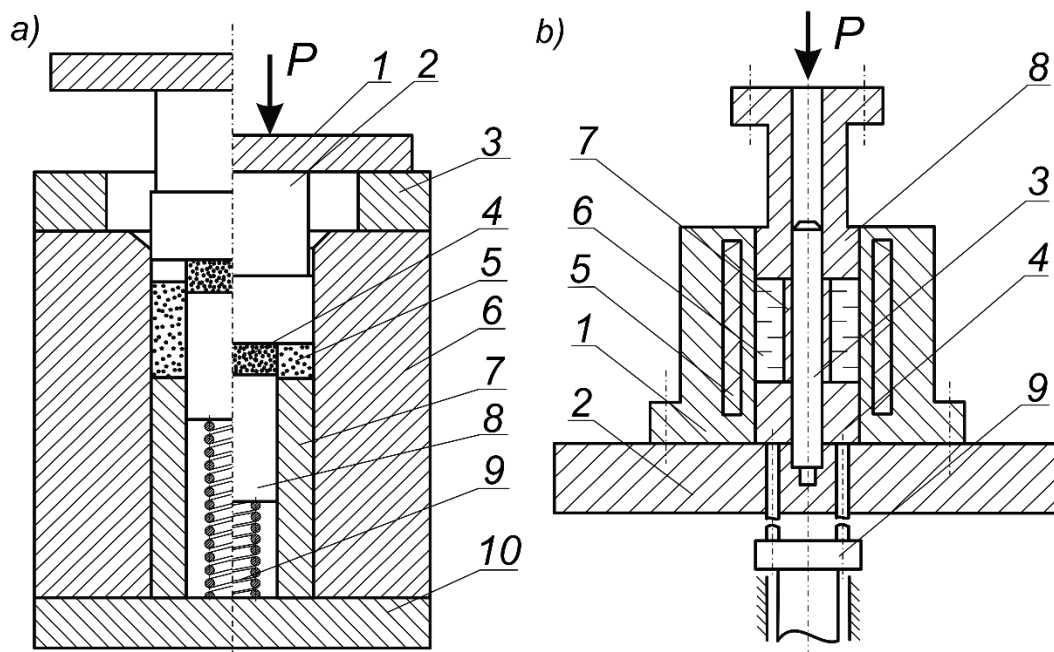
Принципиальные схемы пресс-форм. Схема для прессования спеченных вкладышей с порошком (а): 1 - плита, 2 - верхний пуансон, 3 - упор, 4 - внутренний слой, 5 - наружный слой, 6 - матрица, 7 - нижний упор, 8 - нижний пуансон, 9 - пружина, 10 - основание. Схема для штамповки вкладыша с жидким металлом (б): 1 - матрица, 2 - нижняя плита, 3 - оправка, 4 - опора, 5 - нагревательные элементы, 6 - жидкий алюминий, 7 - вкладыш, 8 - пуансон, 9 - выталкиватель.
